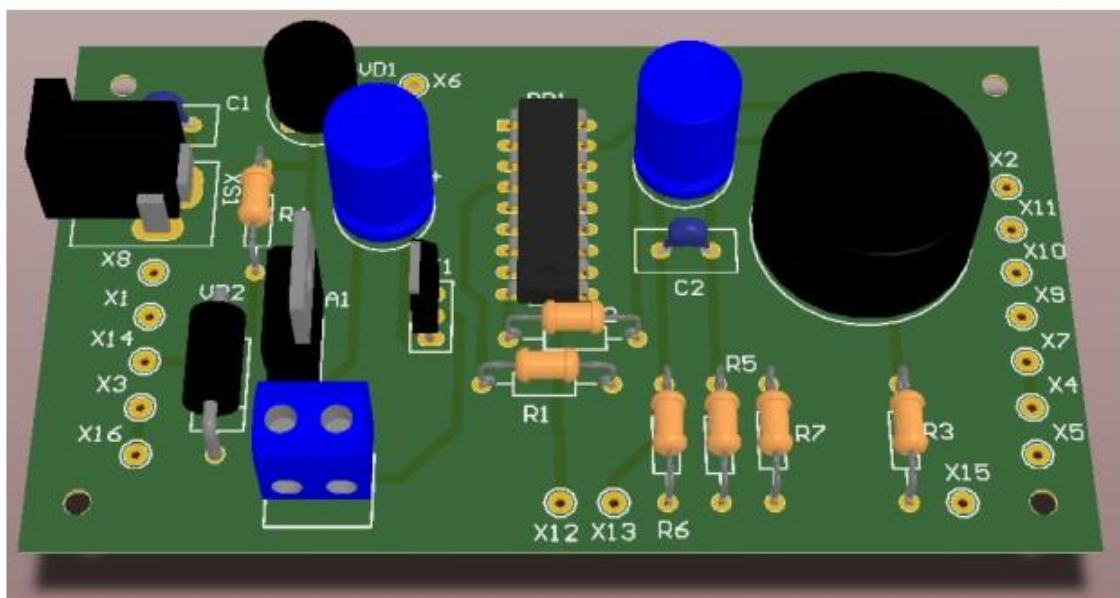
3D модель друкованої плати робоча частина
